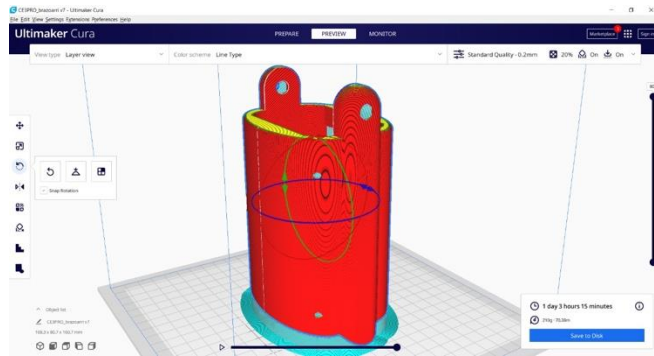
Vista isométrica de las piezas a imprimir en Resina
